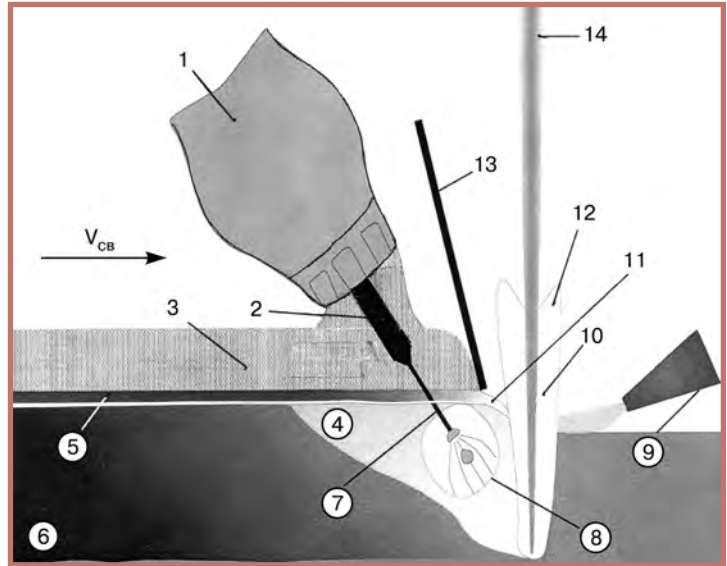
Схема гибридной лазерно-дуговой сварки под флюсом (LUPuS): 1 — бункер для флюса; 2 — контактный мундштук; 3 — флюс; 4 — ванна жидкого металла; 5 — шлаковая корка; 6 — металл сварного шва; 7 — сварочная проволока; 8 — зона горения дуги; 9 — сопло подачи гелия; 10 — парогазовый канал; 11 — расплавленный флюс; 12 — исходящие плазма и пары металла; 13 — разделительная пластина; 14 — лазерный пучок
